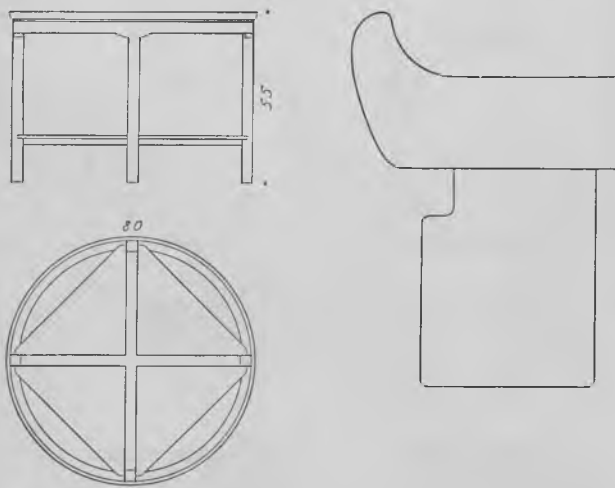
Lavt, rundt bord med bakkeformet plade.
